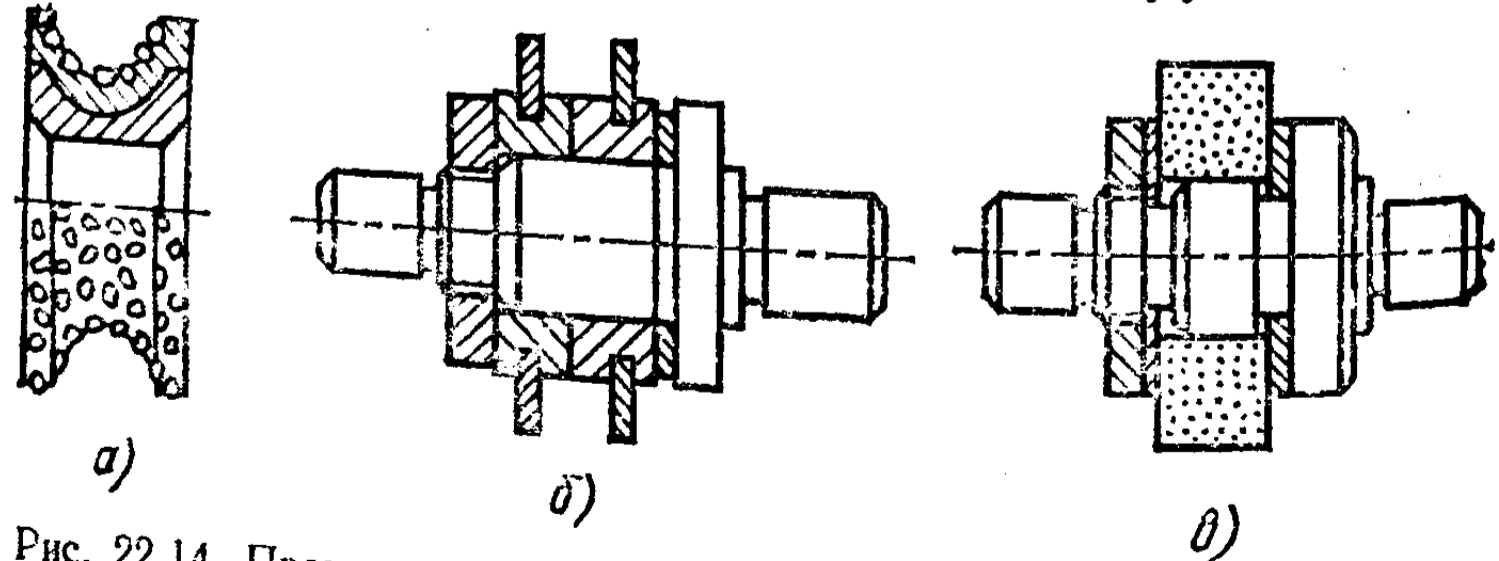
Правящие инструменты: а — алмазно-металлический ролик; б — твердосплавные ролики; в — круг
